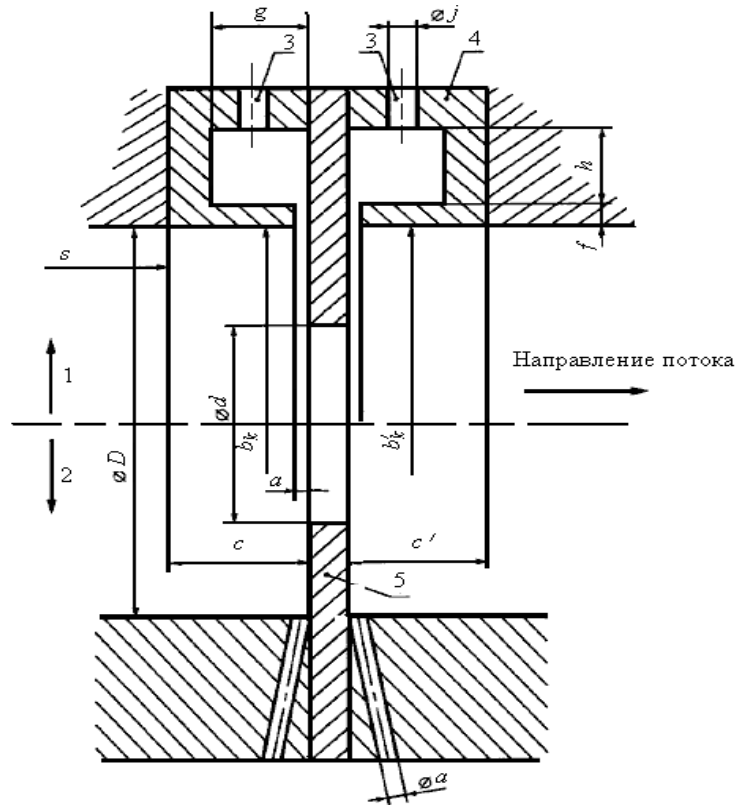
Схема расположения угловых отверстий для отбора давления:
